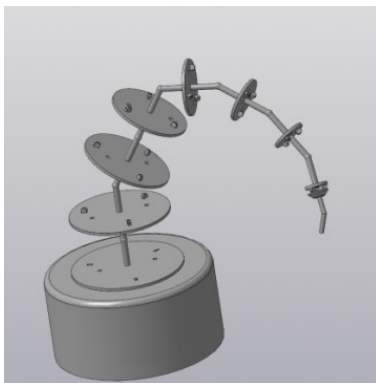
Сварочный робот на базе гибкого манипулятора
